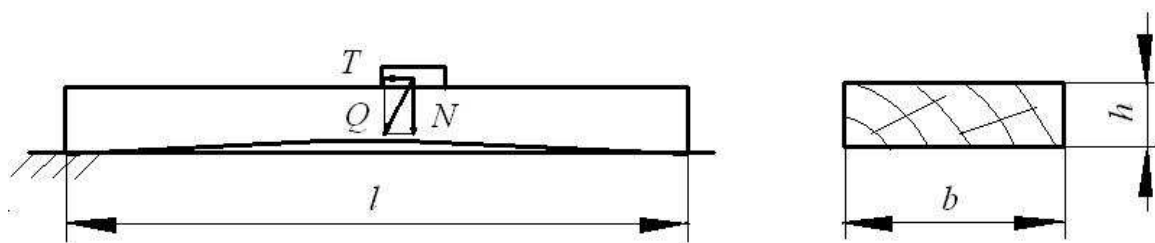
Схема перемещения заготовки по столу фуговального станка
